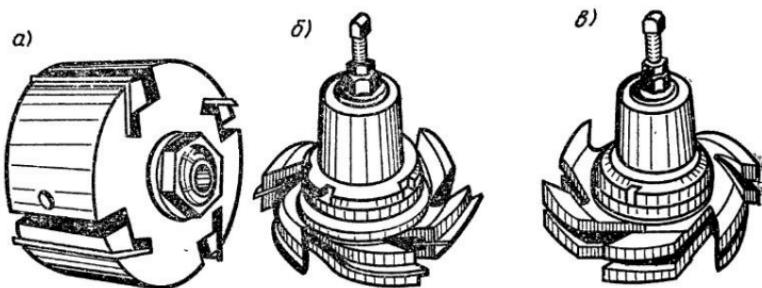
Комплект режущего инструмента фуговального станка С26-2, предназначенного для обработки досок пола
